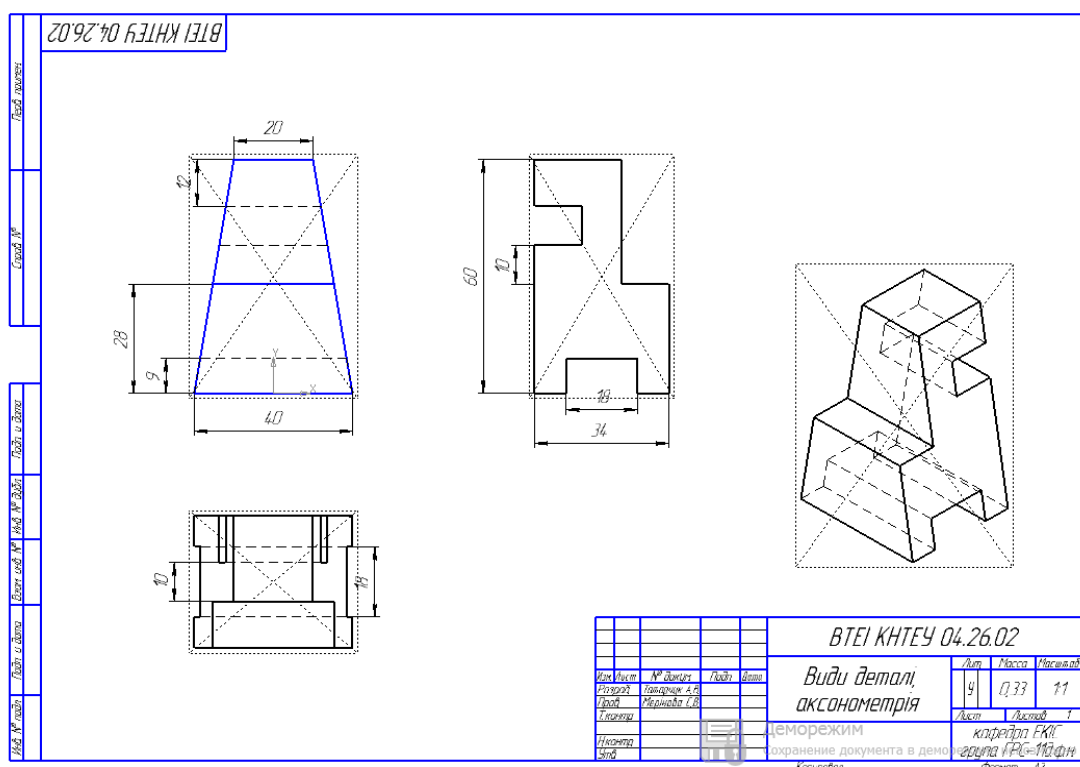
Приклад другого креслення деталі з аксонометрією
